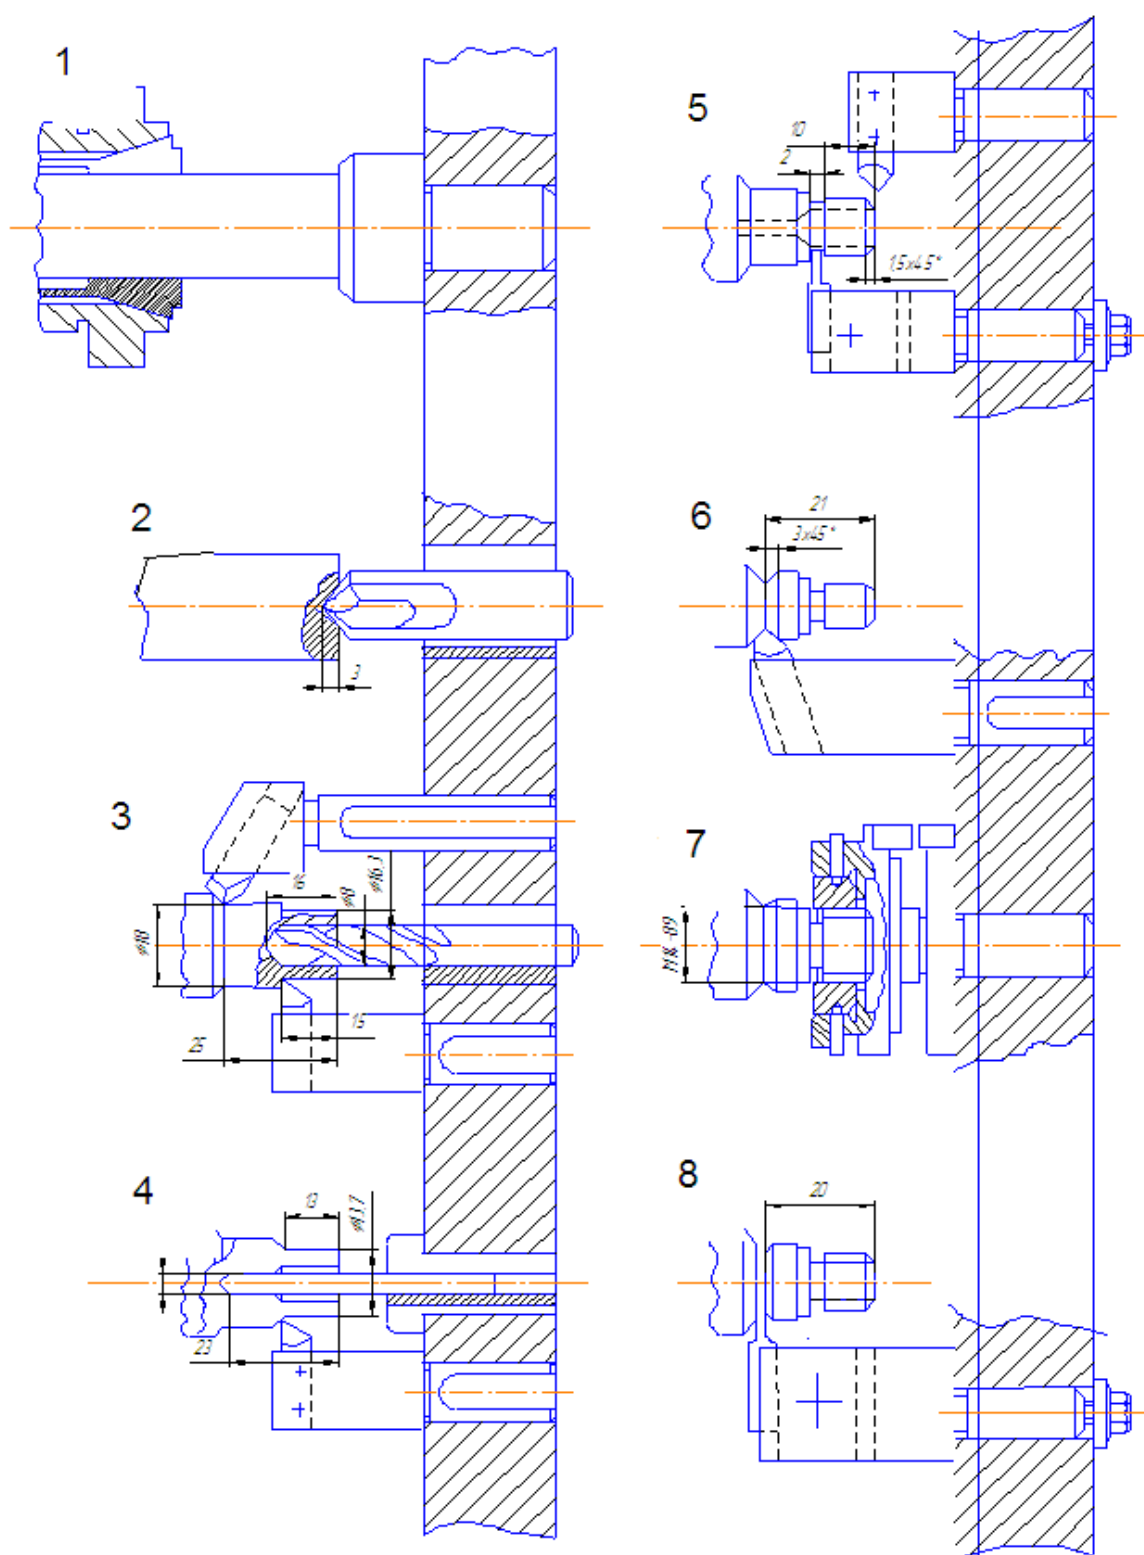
Технологическая наладка токарно-револьверного станка мод. 1336М на обработку детали «сопло»
